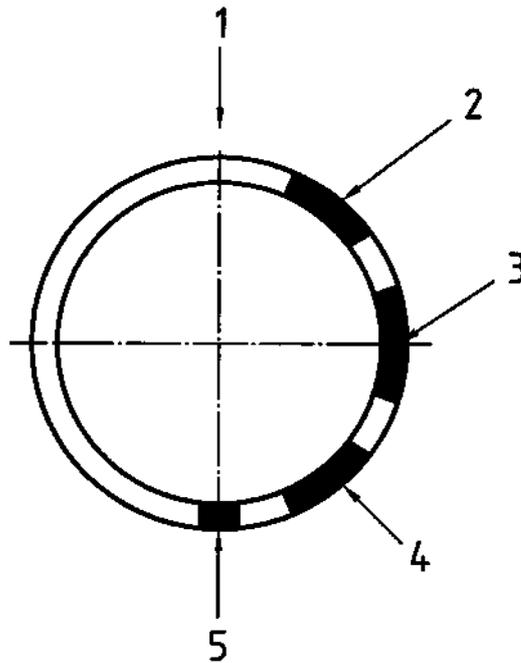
Расположение образцов для испытаний стыкового соединения при сварке труб
